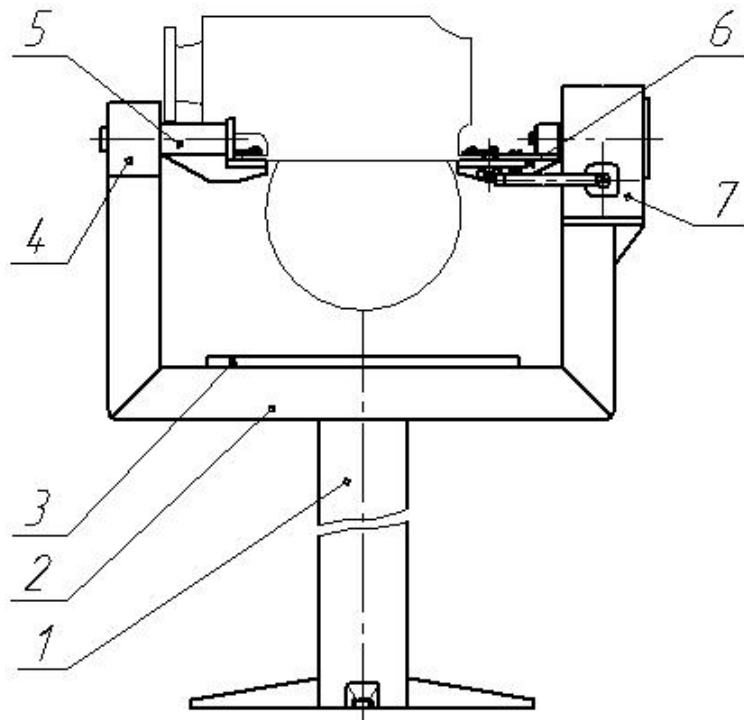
Схема стенду для розбирання та складання редукторів.
